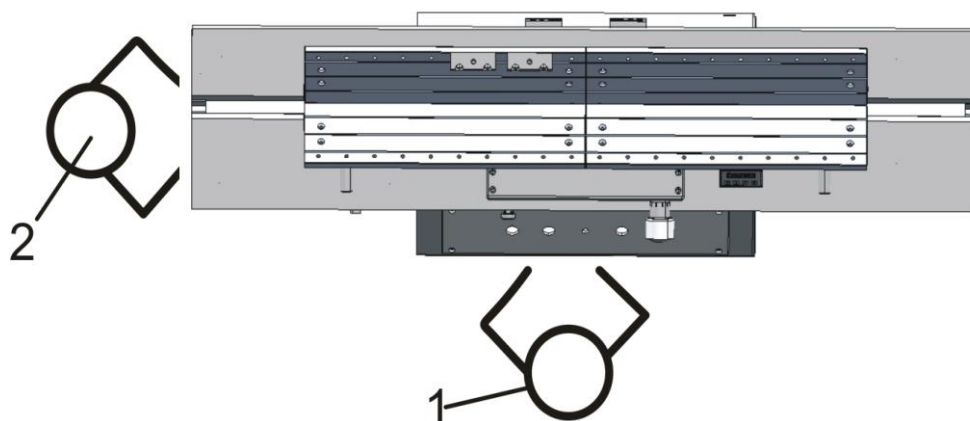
Draufsicht der Kantenfräsmaschine mit Position der Arbeitsplätze
